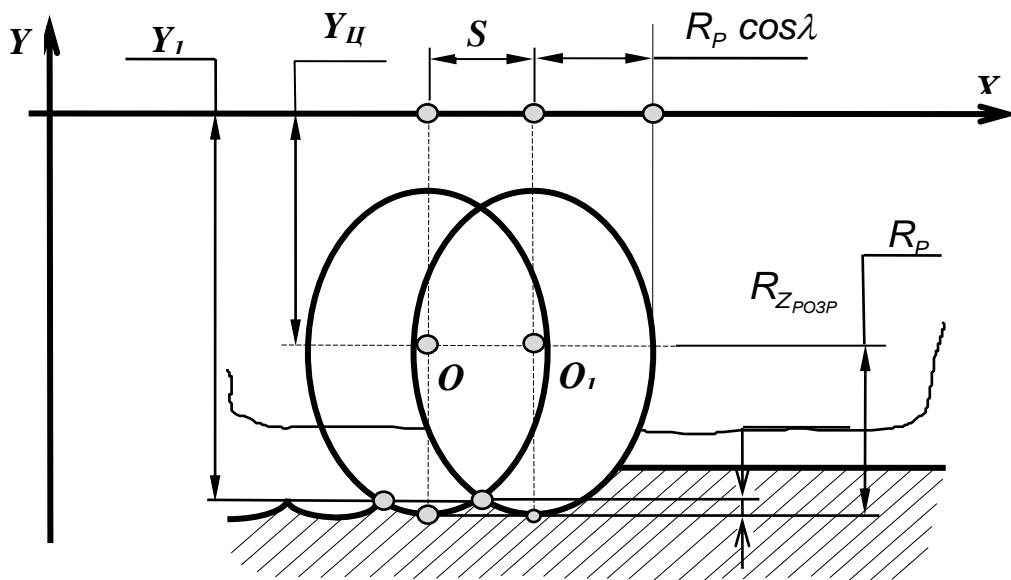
Схема розрахункової шорсткості обробленої поверхні
